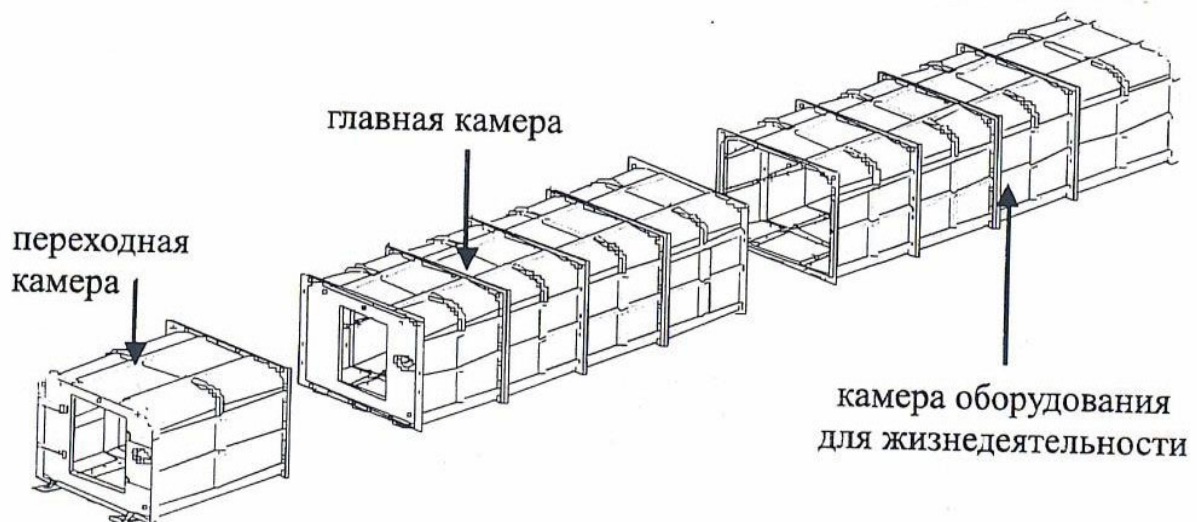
Схема конструкции корпуса камеры спасения
